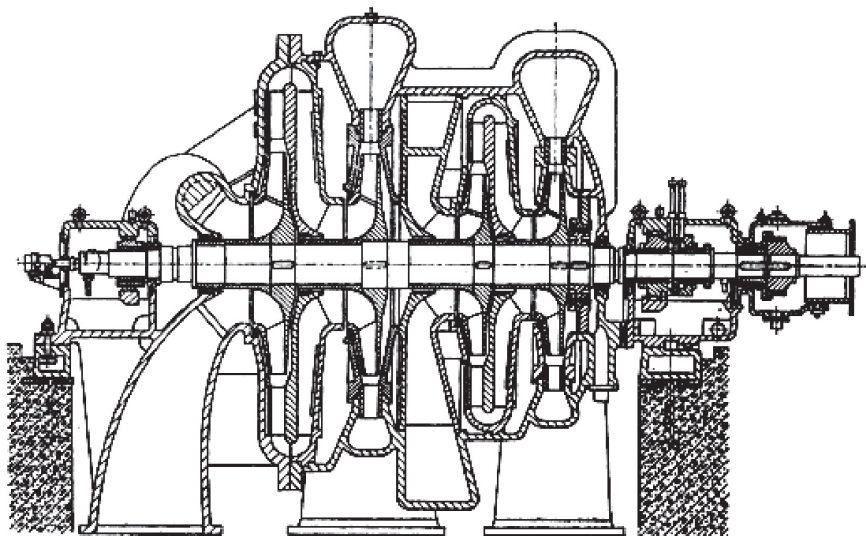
Первый корпус двухкорпусного центробежного компрессора
